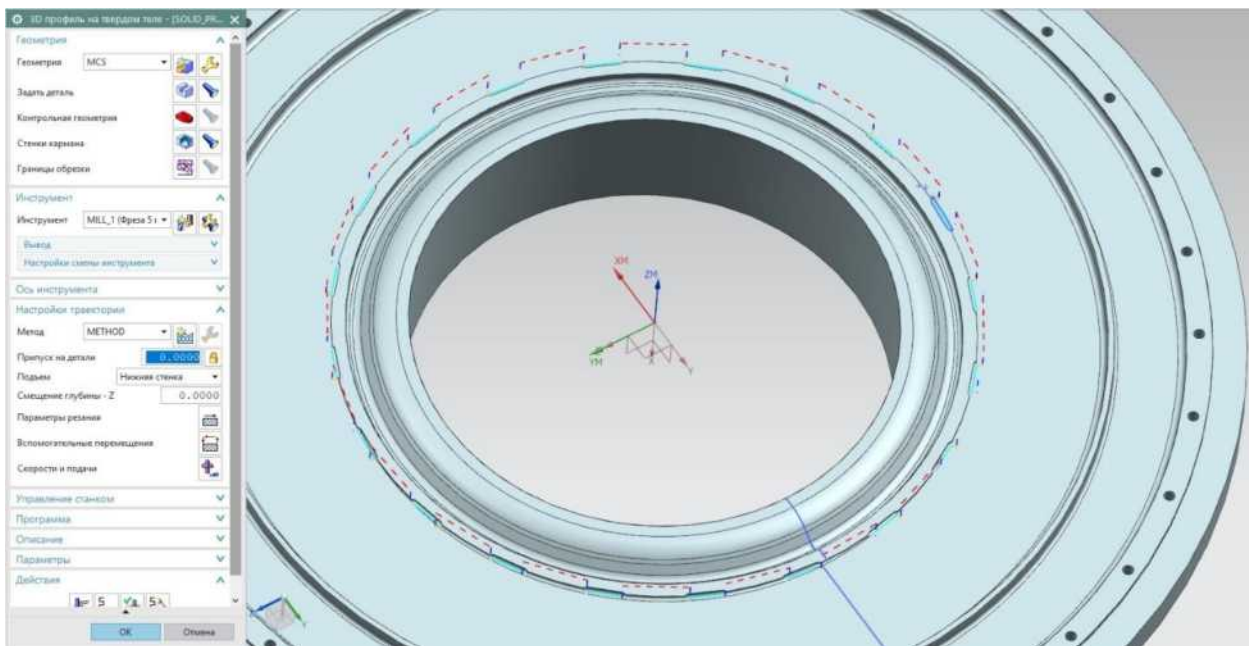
Траектория обработки на опер. 095 Фрезерна з ЧПК.
